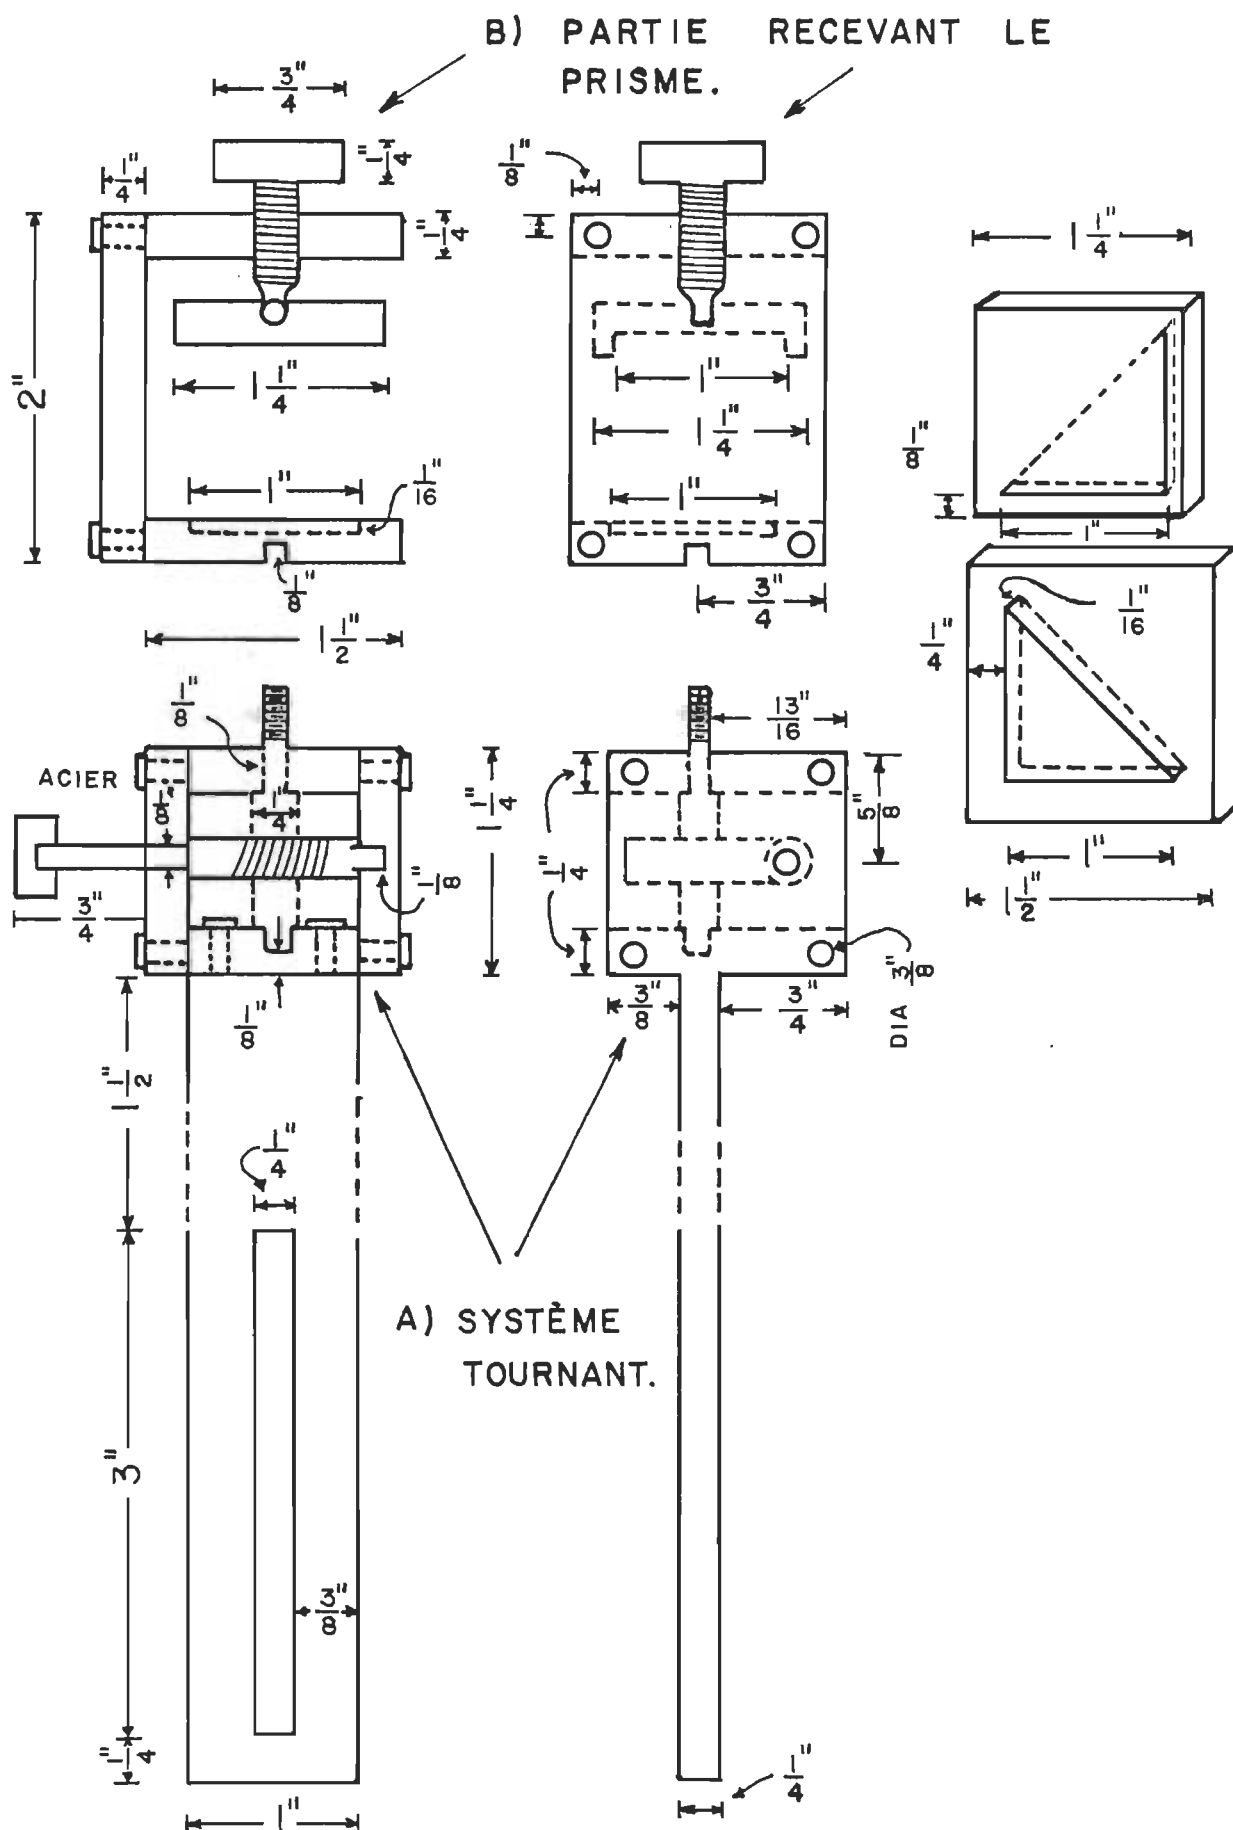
Plan détaillé de la section horizontale du support recevant le prisme.
